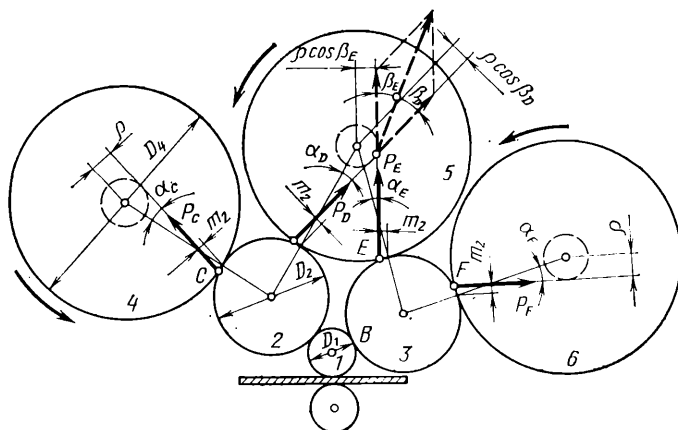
Силы, действующие на основные опорные валки 12-валкового стана
